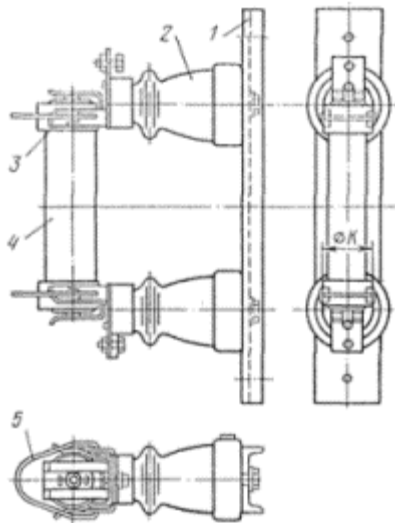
Предохранитель типа ПКТ: 1- цоколь; 2- опорный изолятор; 3- контакт; 4- патрон; 5- замок
